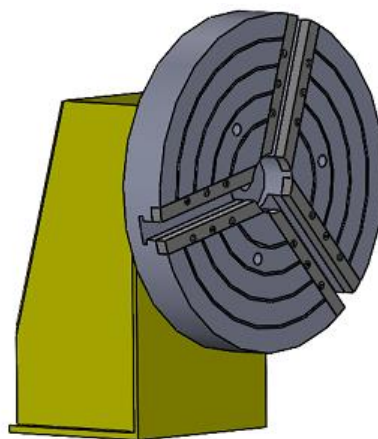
Aplicação do prato da bucha fixadora na estrutura existente
